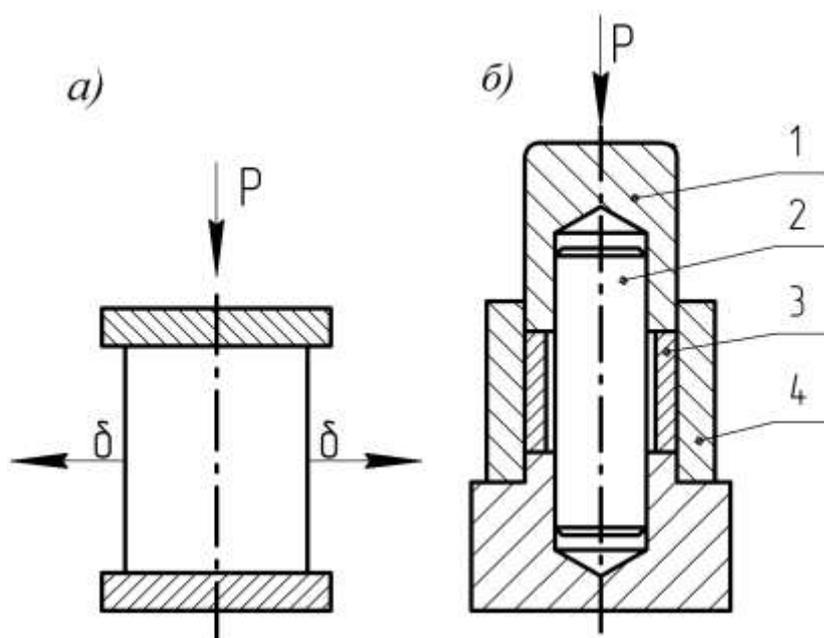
Осадка: *а* – схема обработки; *б* – приспособление для осадки втулок; 1 – пуансон; 2 и 4 – оправки; 3 – восстанавливаемая деталь
